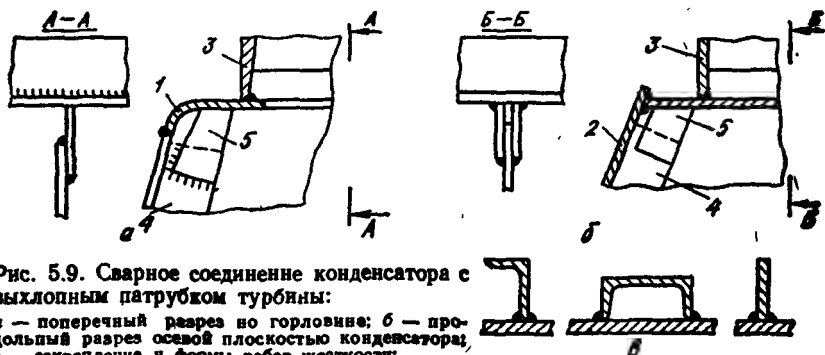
Сварное соединение конденсатора с выпускным патрубком турбины:
